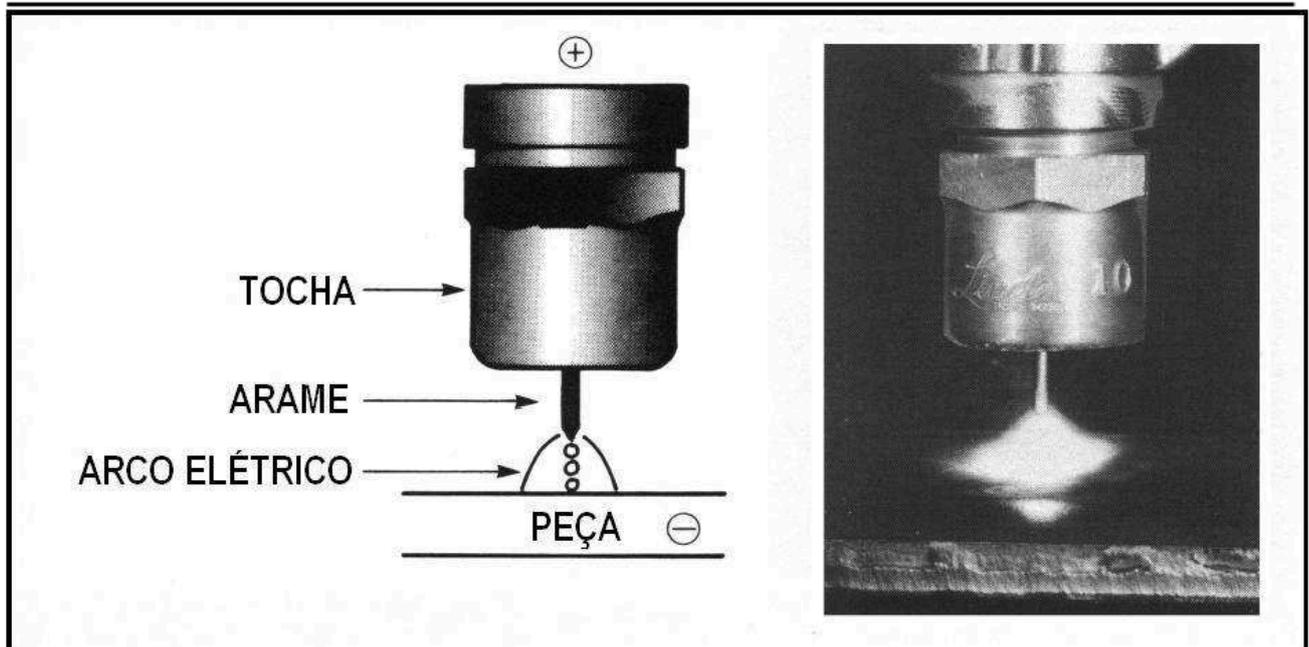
Técnica de soldagem por arco em aerossol (spray) (ESAB MIG)
